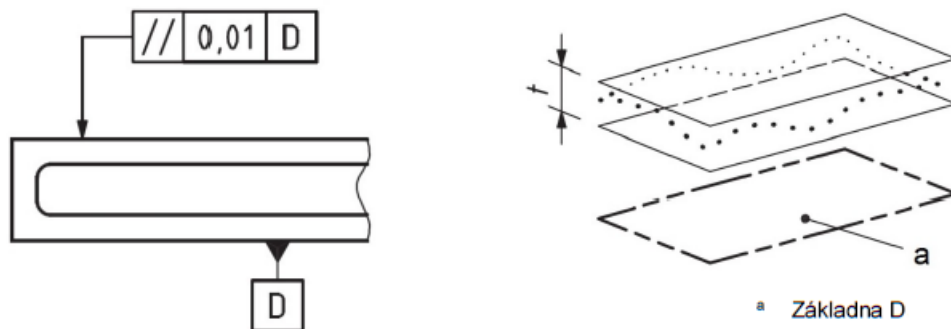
Indikace tolerance rovnoběžnosti lineárních prvků [14]
